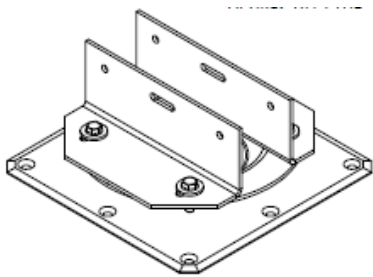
V1: Punkthalter für Dachpaneele, Holz
